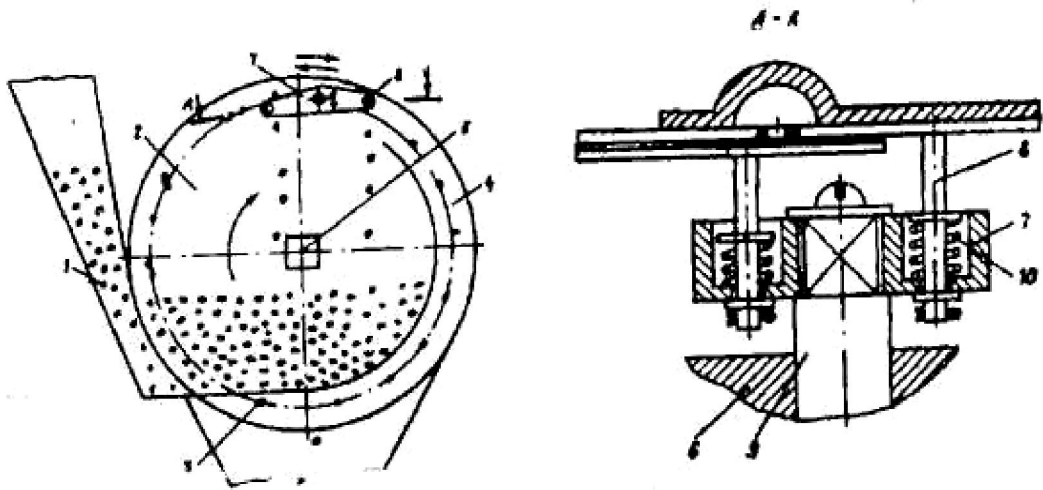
Апарат з новим вилковим відбивачем: 1 - камера з насінням; 2 - висівний диск; 3 - наскрізні отвори диска, які розташовані по колу 4; 5 - вал; 6 - корпус; 7 - вилковий відбивач; 8 - зуби відбивача; 9 - поворотна вісь відбивача; 10 - пружини
